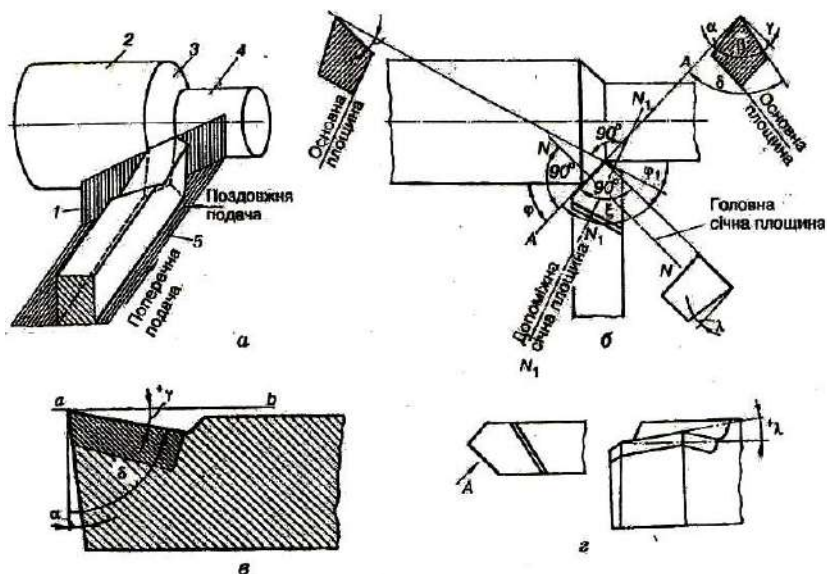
Поверхні на оброблювальній заготовці, координатні площини та геометричні параметри різця
